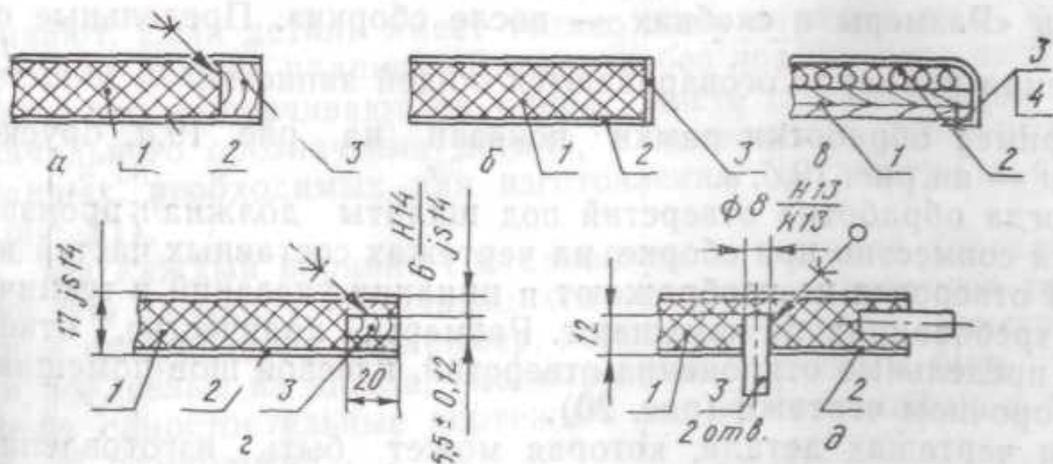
Детали сборочных единиц, не требующих разработки чертежей в соединениях:
